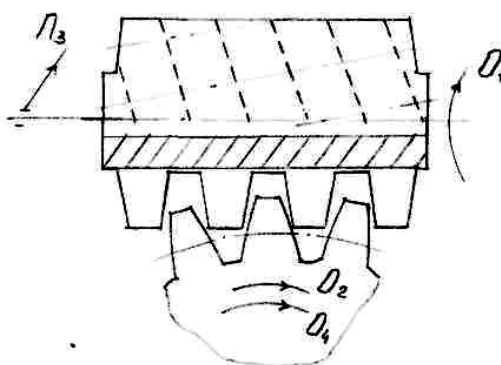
Схема обробки черв'ячною фрезою
